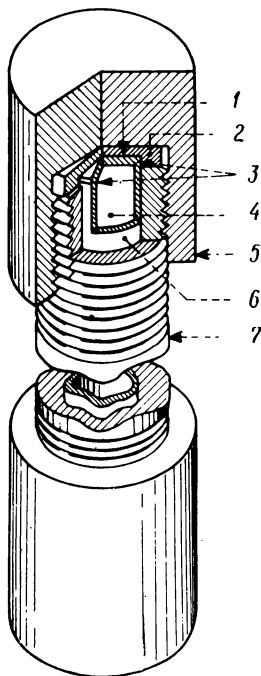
Автоклав со сварным вкладышем [49].
